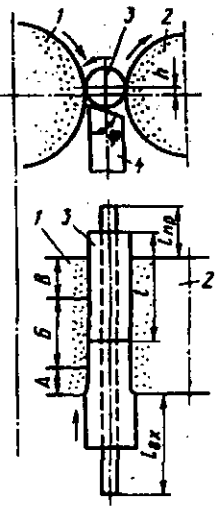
Схема и рабочий цикл бесцентрового проходного шлифования
